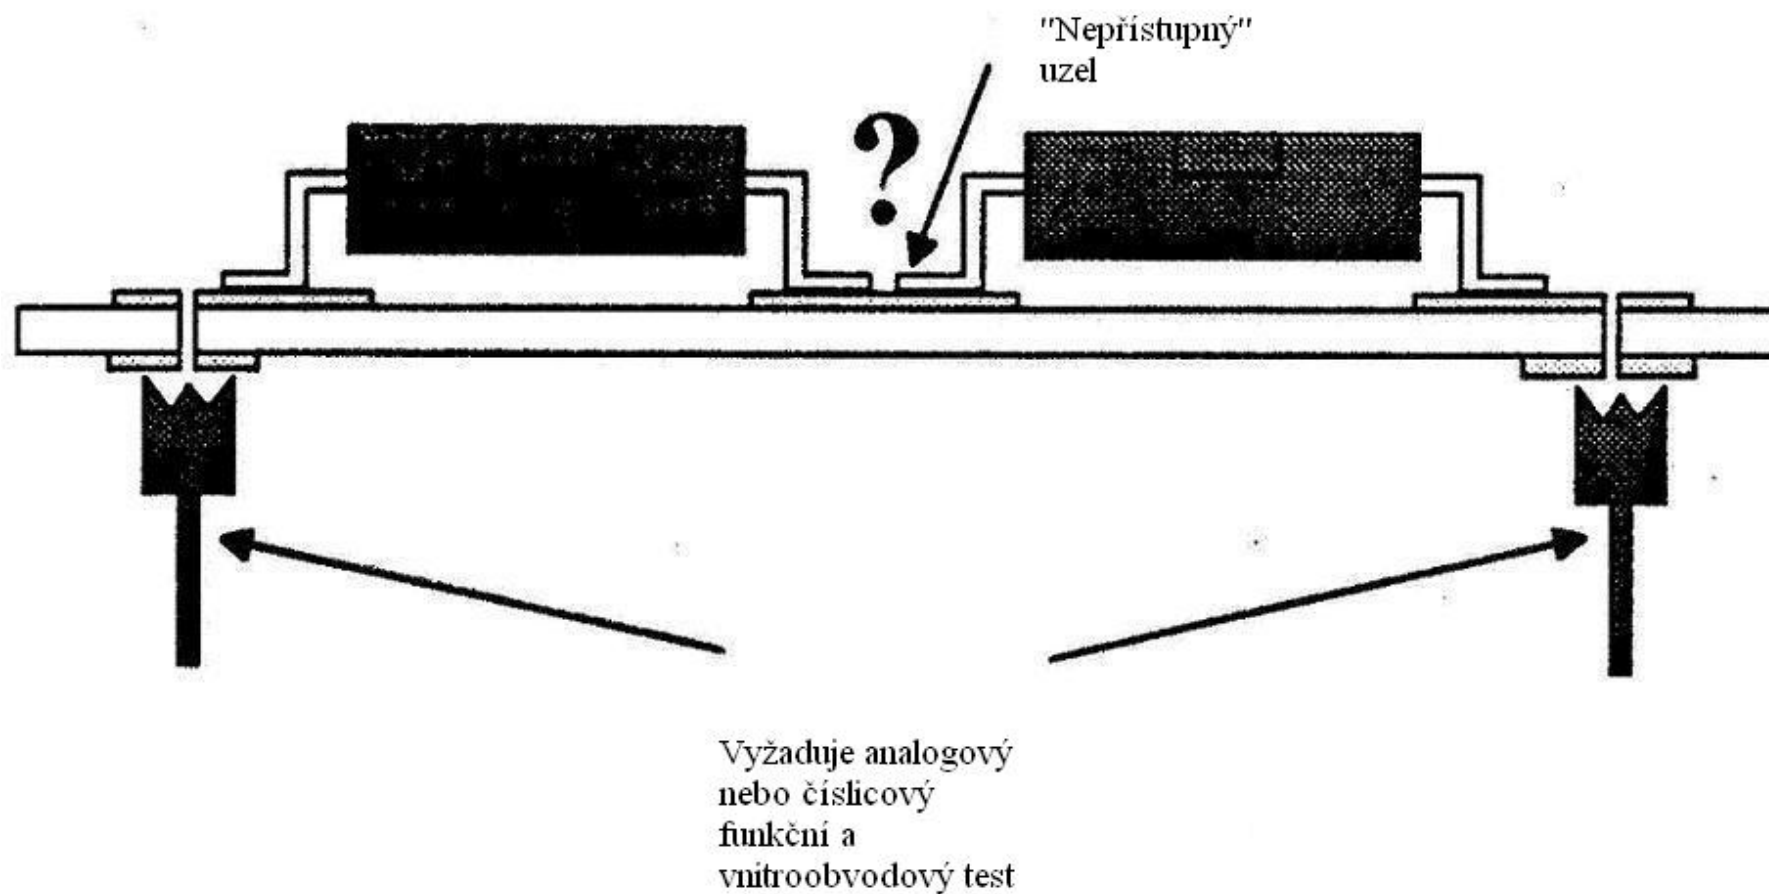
Ilustrace možnosti připojení kontaktu u testeru
